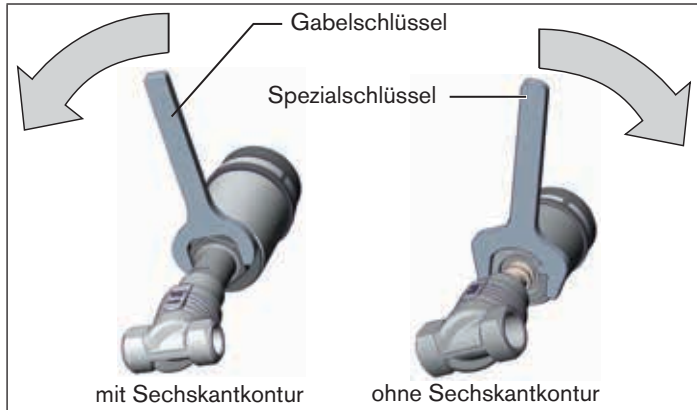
Drehen mit Gabelschlüssel / Spezialschlüssel
